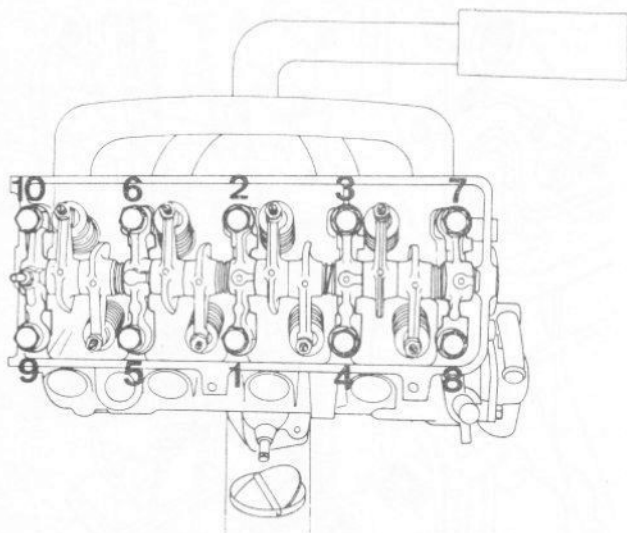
Ordre de serrage/desserrage des boulons de culasse (Sec 6)
